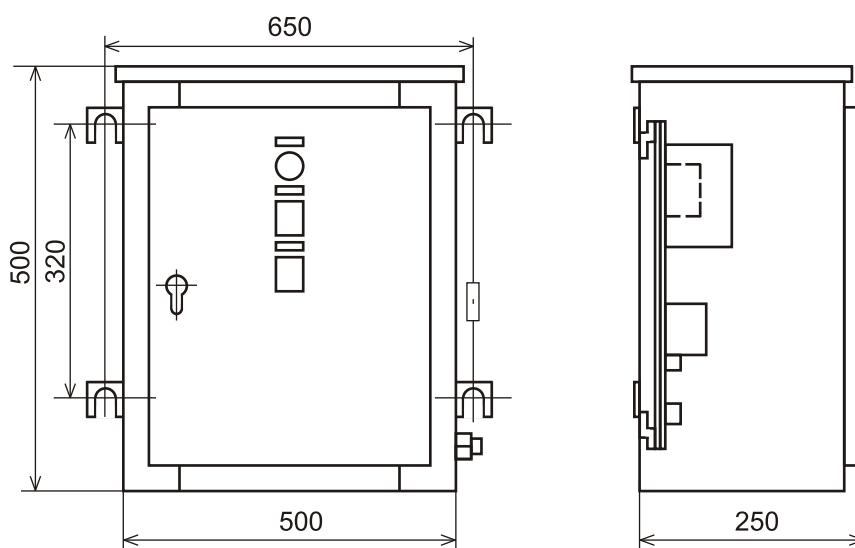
Габаритные и установочные размеры РУСМ
